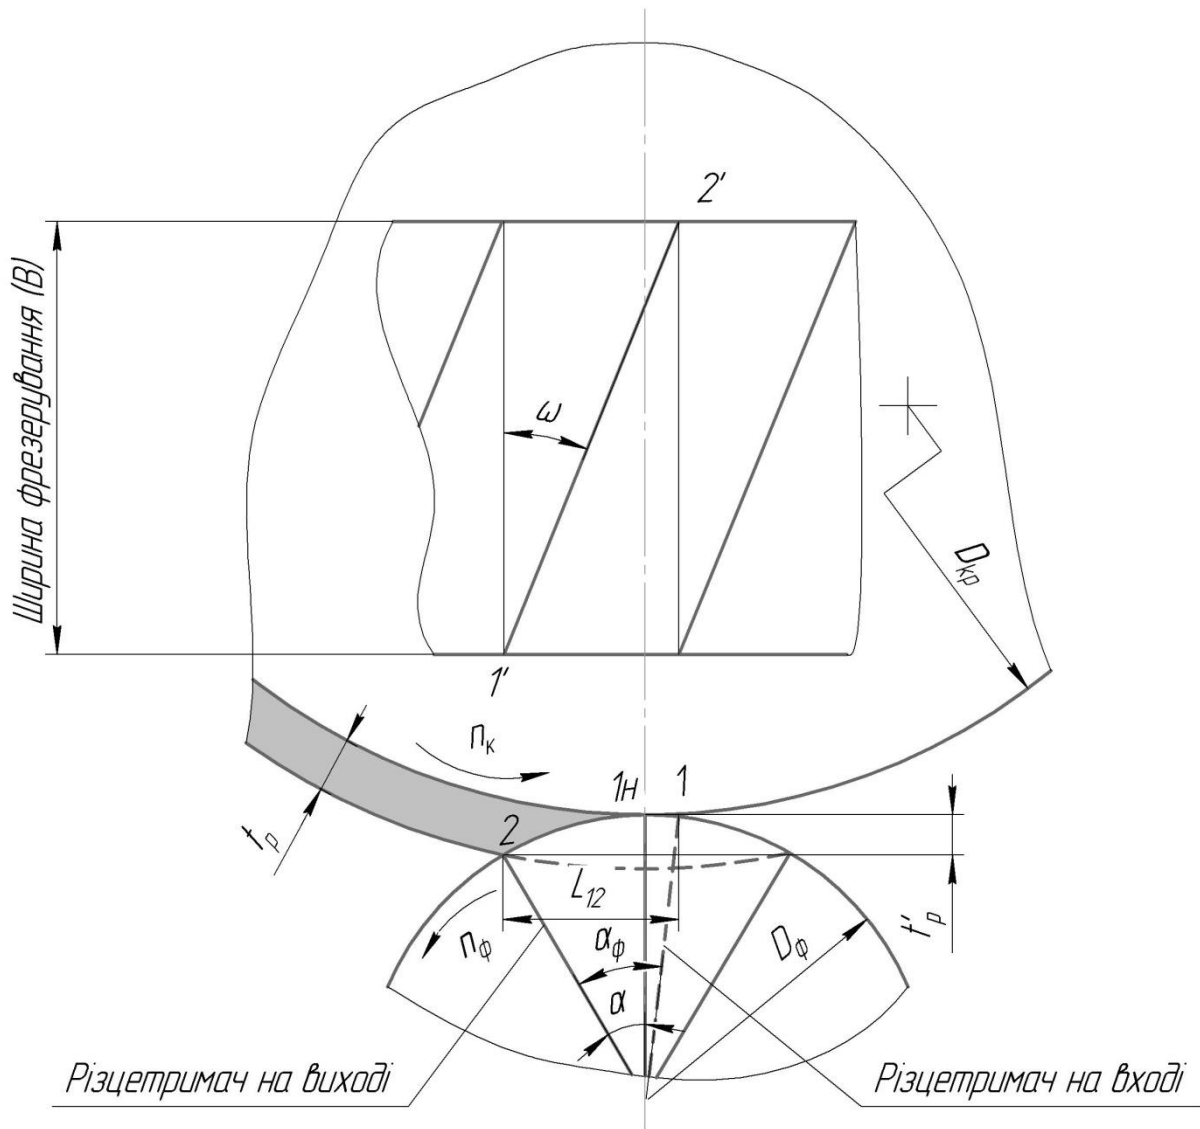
Схема умови рівномірного фрезерування колісної пари
